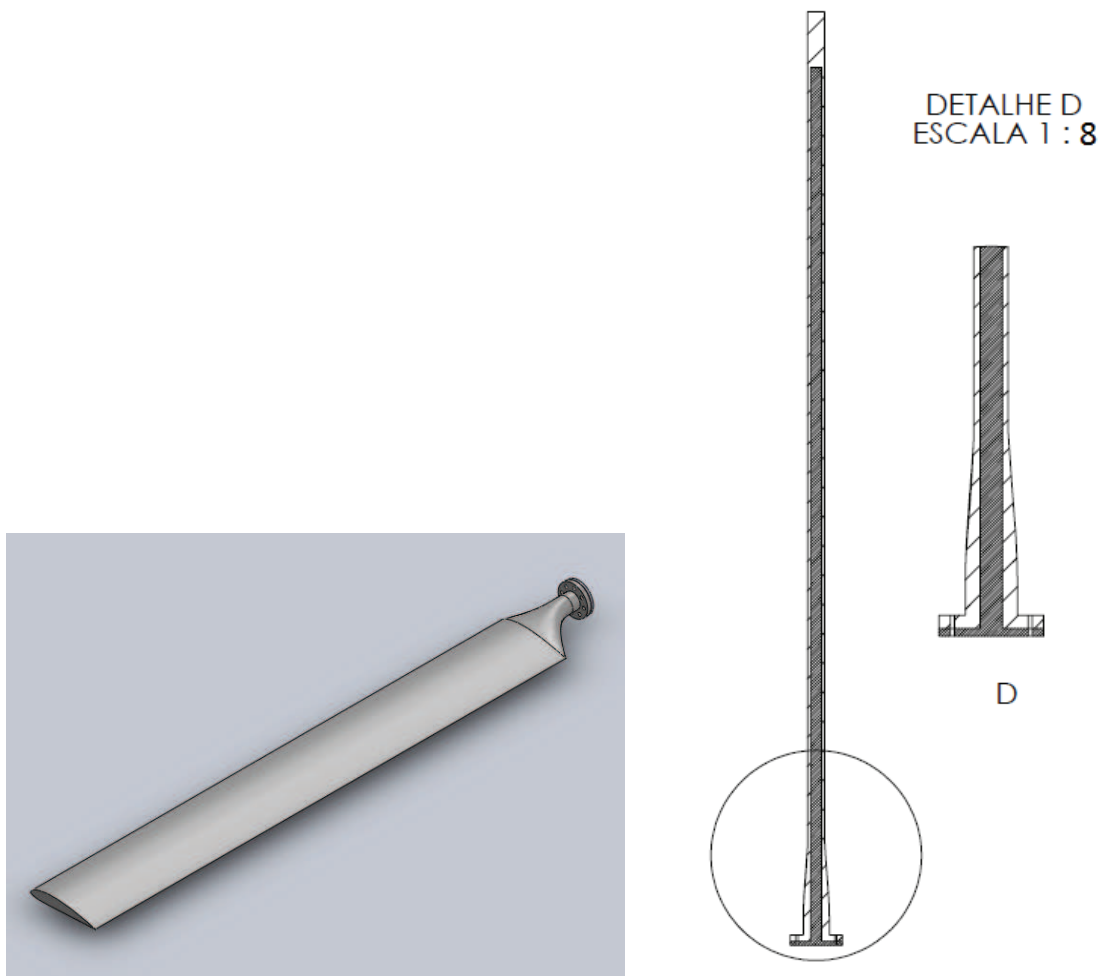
Pá do Rotor e vista de corte com detalhe
